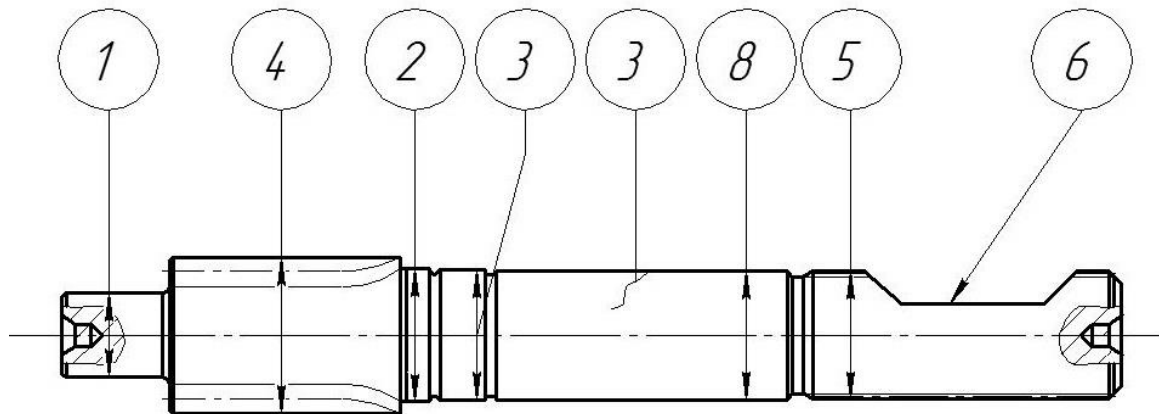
Конструкція вала-шестерні рульового механізму.
